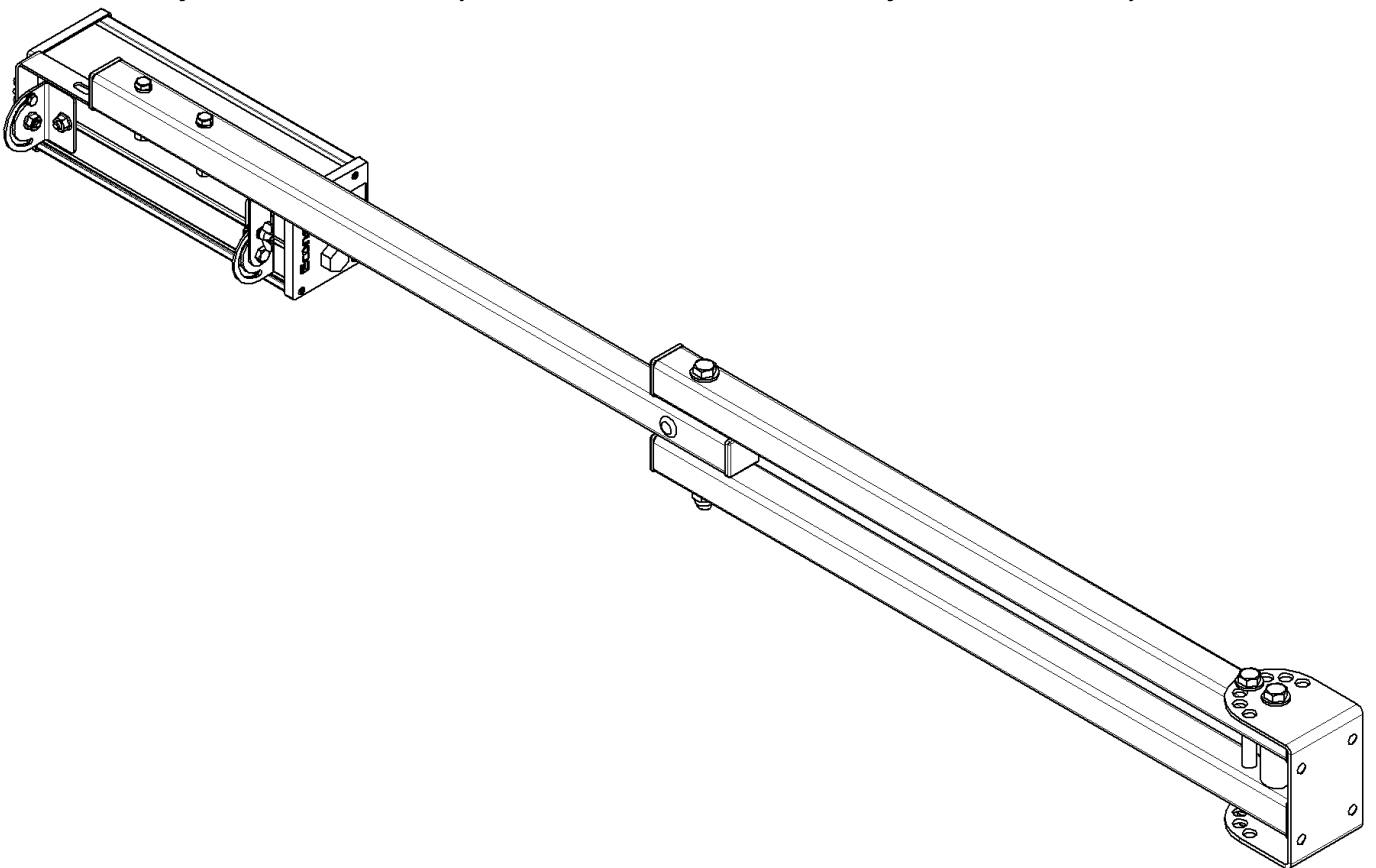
Габаритный чертеж светильника Esonex Board WD
